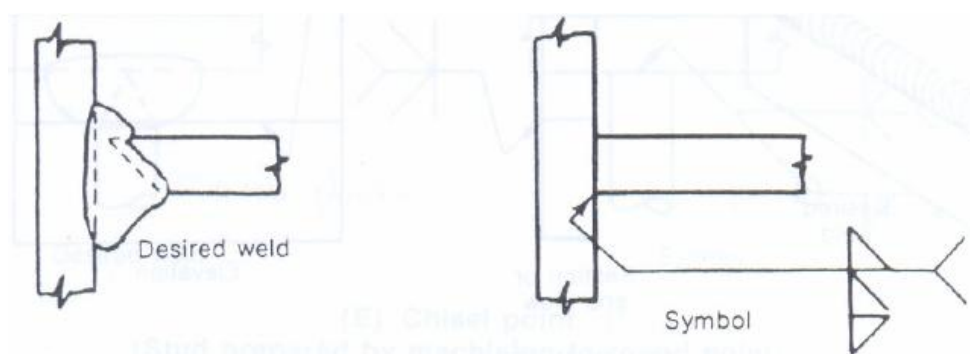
Soldadura tipo ranura simple y doble filete (1).
